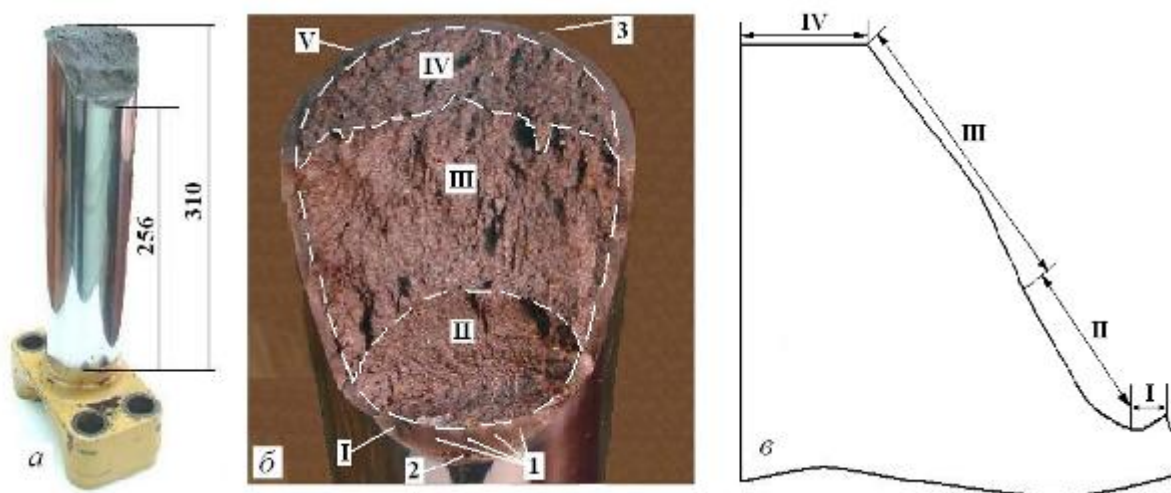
Общий вид (а), поверхность разрушения (б) и схема профиля излома (в) короткого фрагмента штока. I, II, III и IV – зоны разрушения; 1 – места зарождения разрушения; 2 – притертые области; 3 – растрескивания от наружной поверхности
